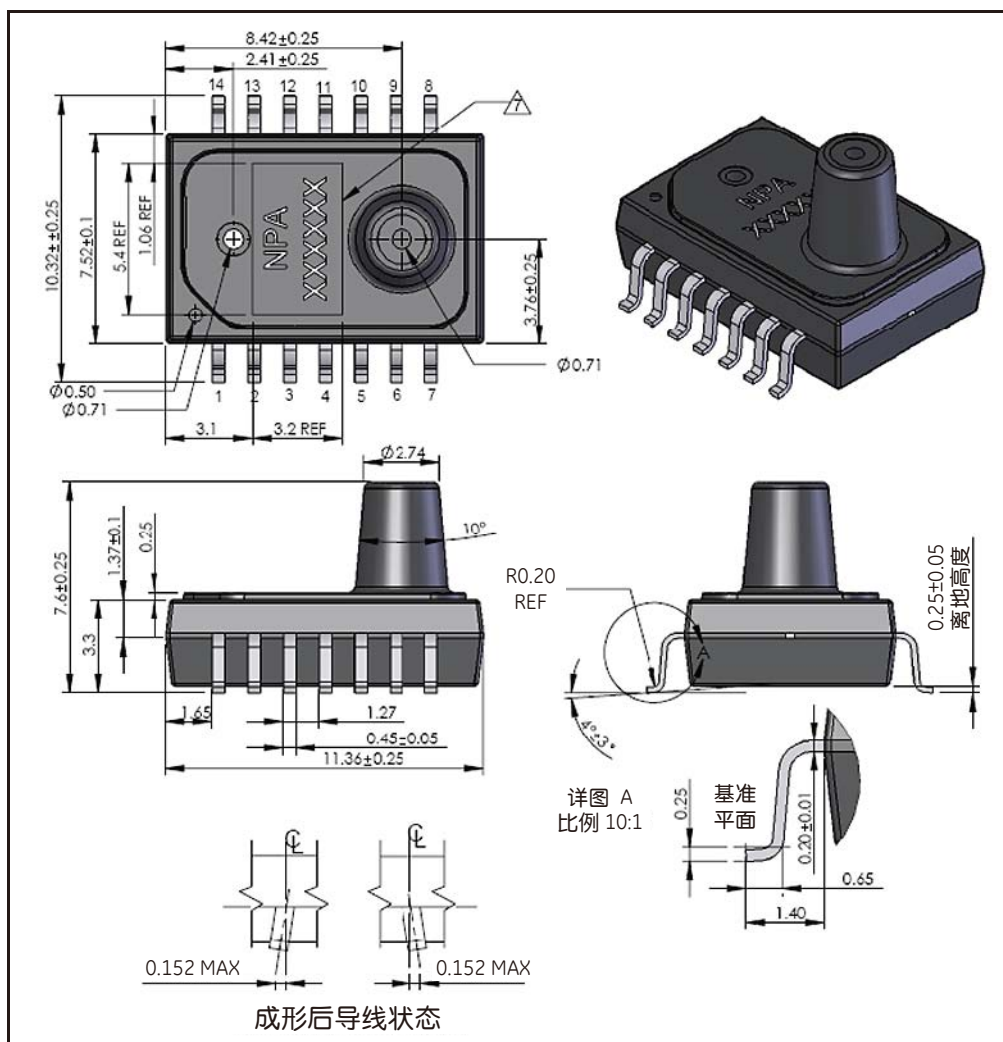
传感器封装尺寸 (mm) - 适合多口径压力接口设计
